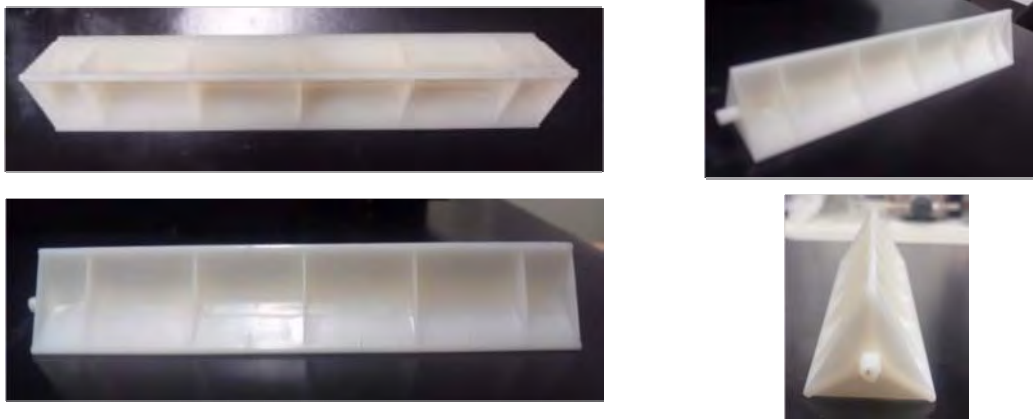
射出成形品の外観 (Appearance of plastic injection molded product) .
